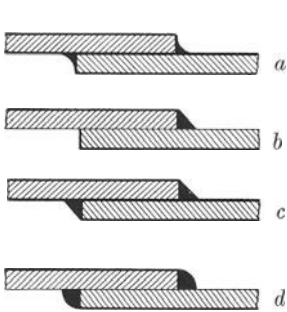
Ausführung der überlappten Schweißung.
